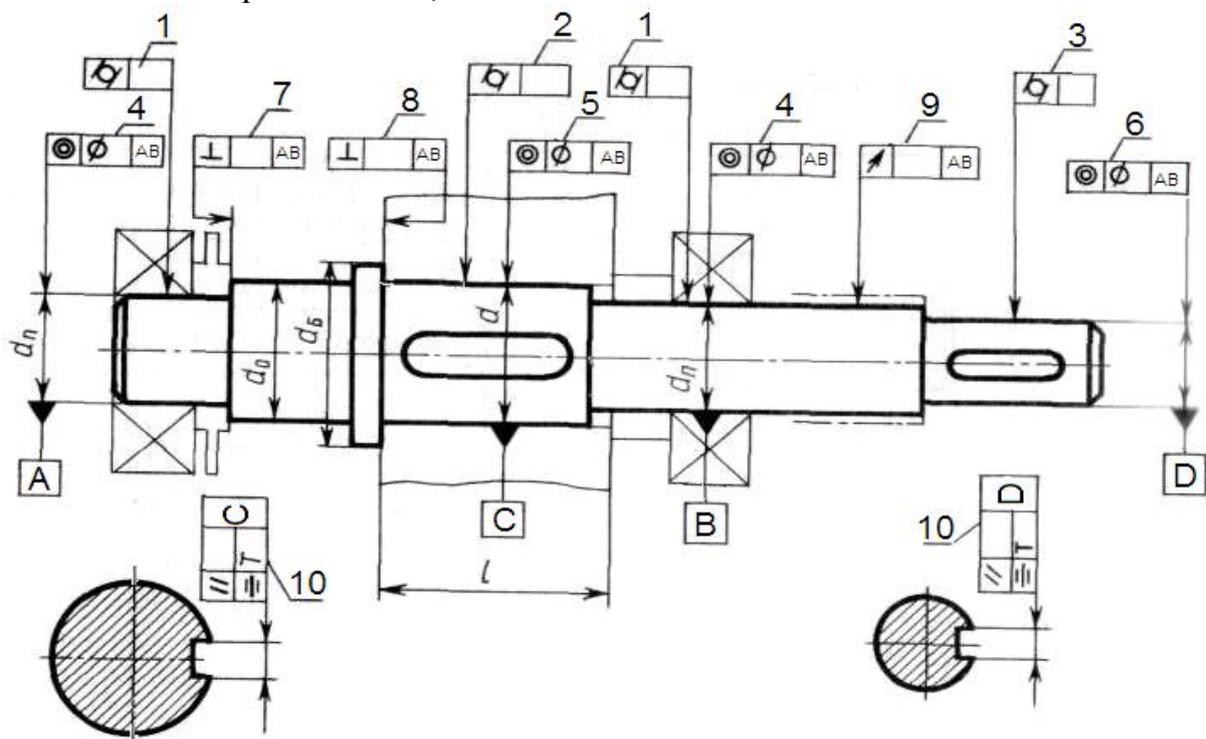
Позначення допусків форми і розташування поверхонь вала на кресленнях
